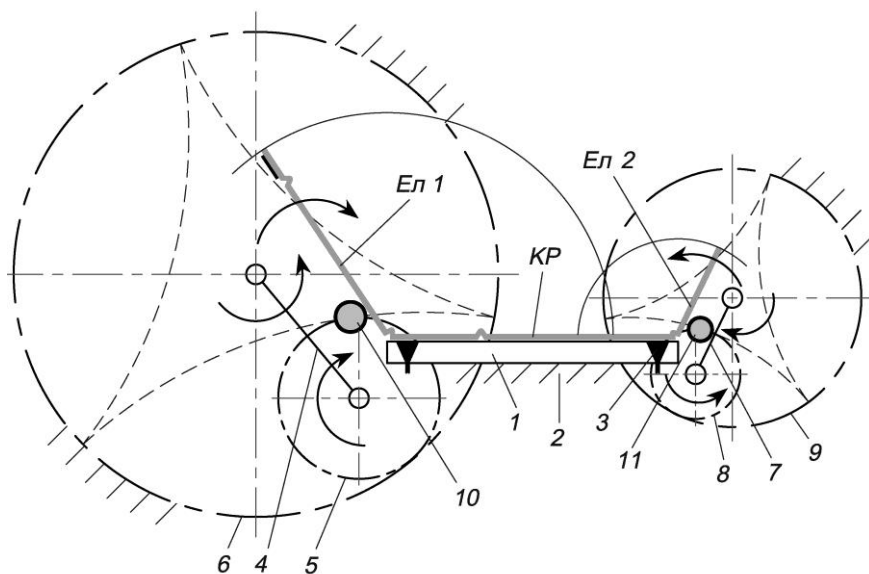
Принципова схема нового пристрою для фальцювання КР
